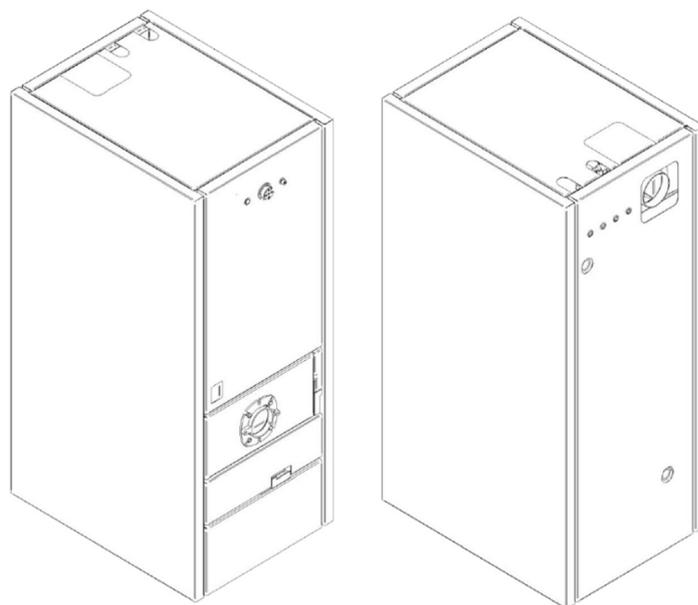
Vues de 3/4 Face et arrières de la chaudière
